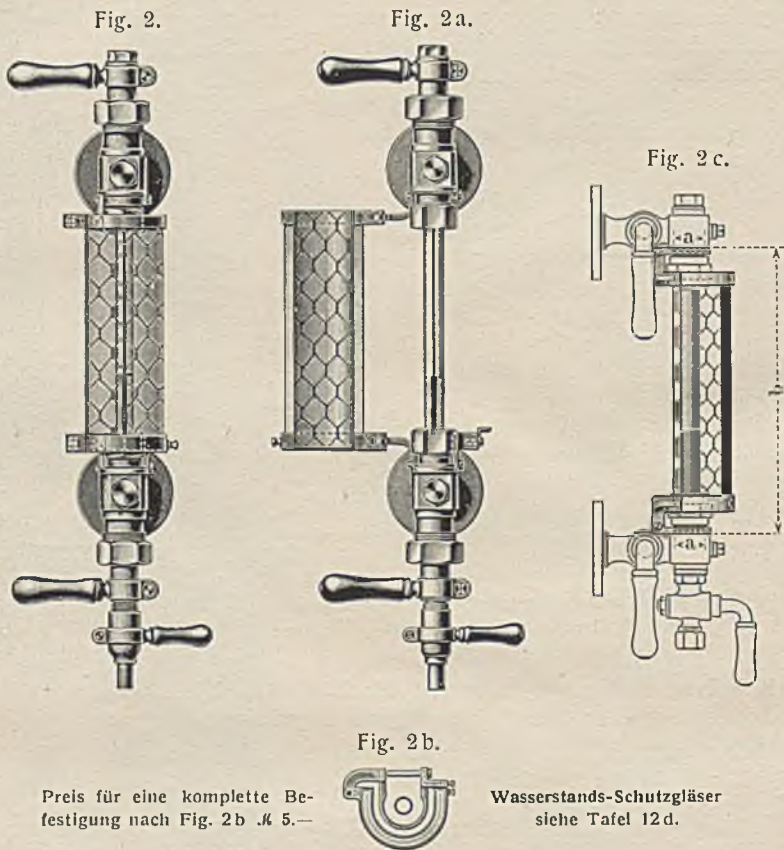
zeigt die Befestigung der Glashalter mittelst einer durch eine Schraube zusammengezogenen Schelle auf dem Gewindestutzen des Wasserstandshahnkopfes.
